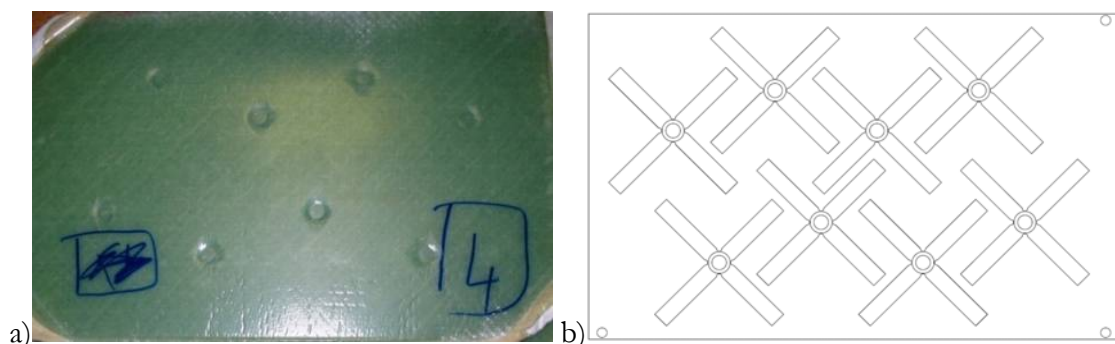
a) Plaque brute avant découpe des éprouvettes et b) empreinte de découpe
